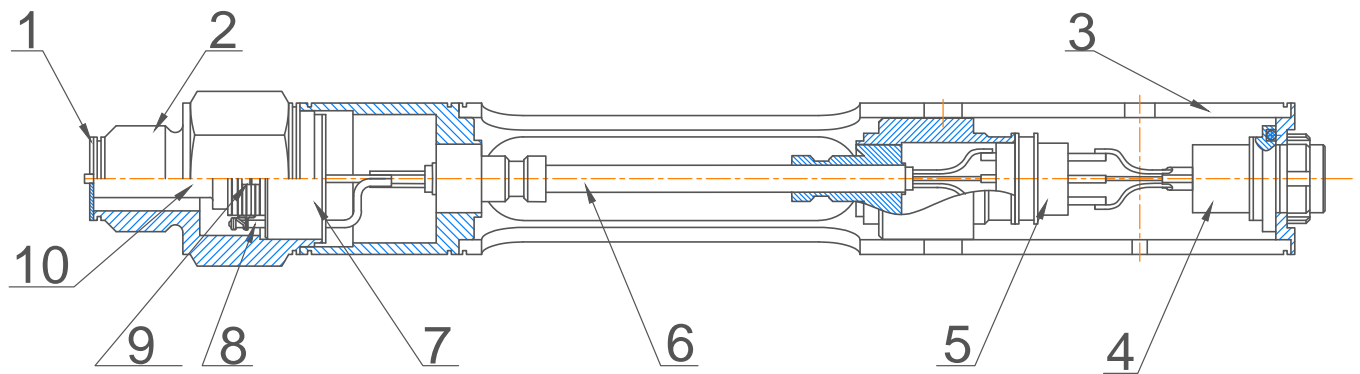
Конструкция МД–45; 1 – мембрана; 2 – корпус; 3 – труба; 4,5 – вилка; 6 – жаропрочный кабель; 7 – основание; 8 – токовывод; 9 – блок пьезокерамический; 10 – шток.
